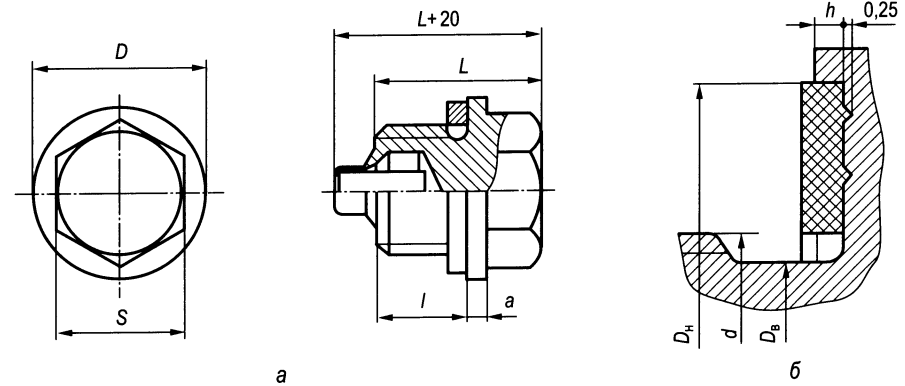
Магнитная пробка с цилиндрической резьбой для маслоспускного отверстия с плоской медной прокладкой (а) и с плоской неметаллической прокладкой (б)
